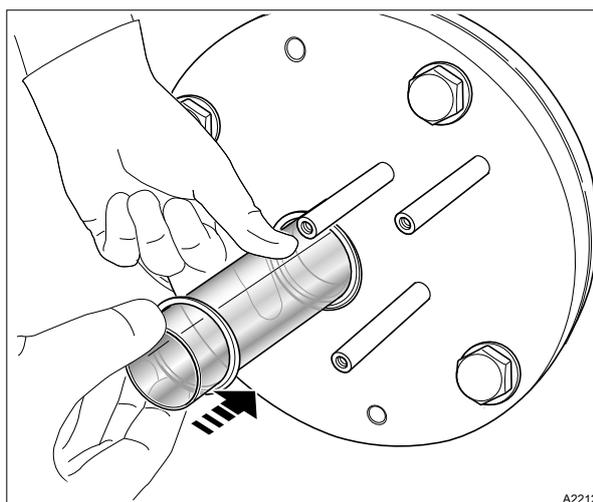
Tube de protection de la lampe UV / Joint torique
